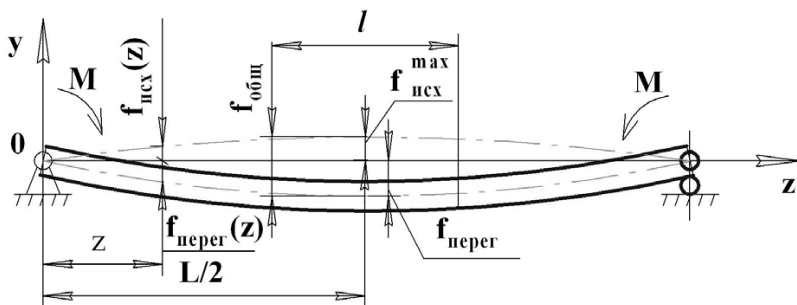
Схема деформации заготовки перед обработкой ППД
